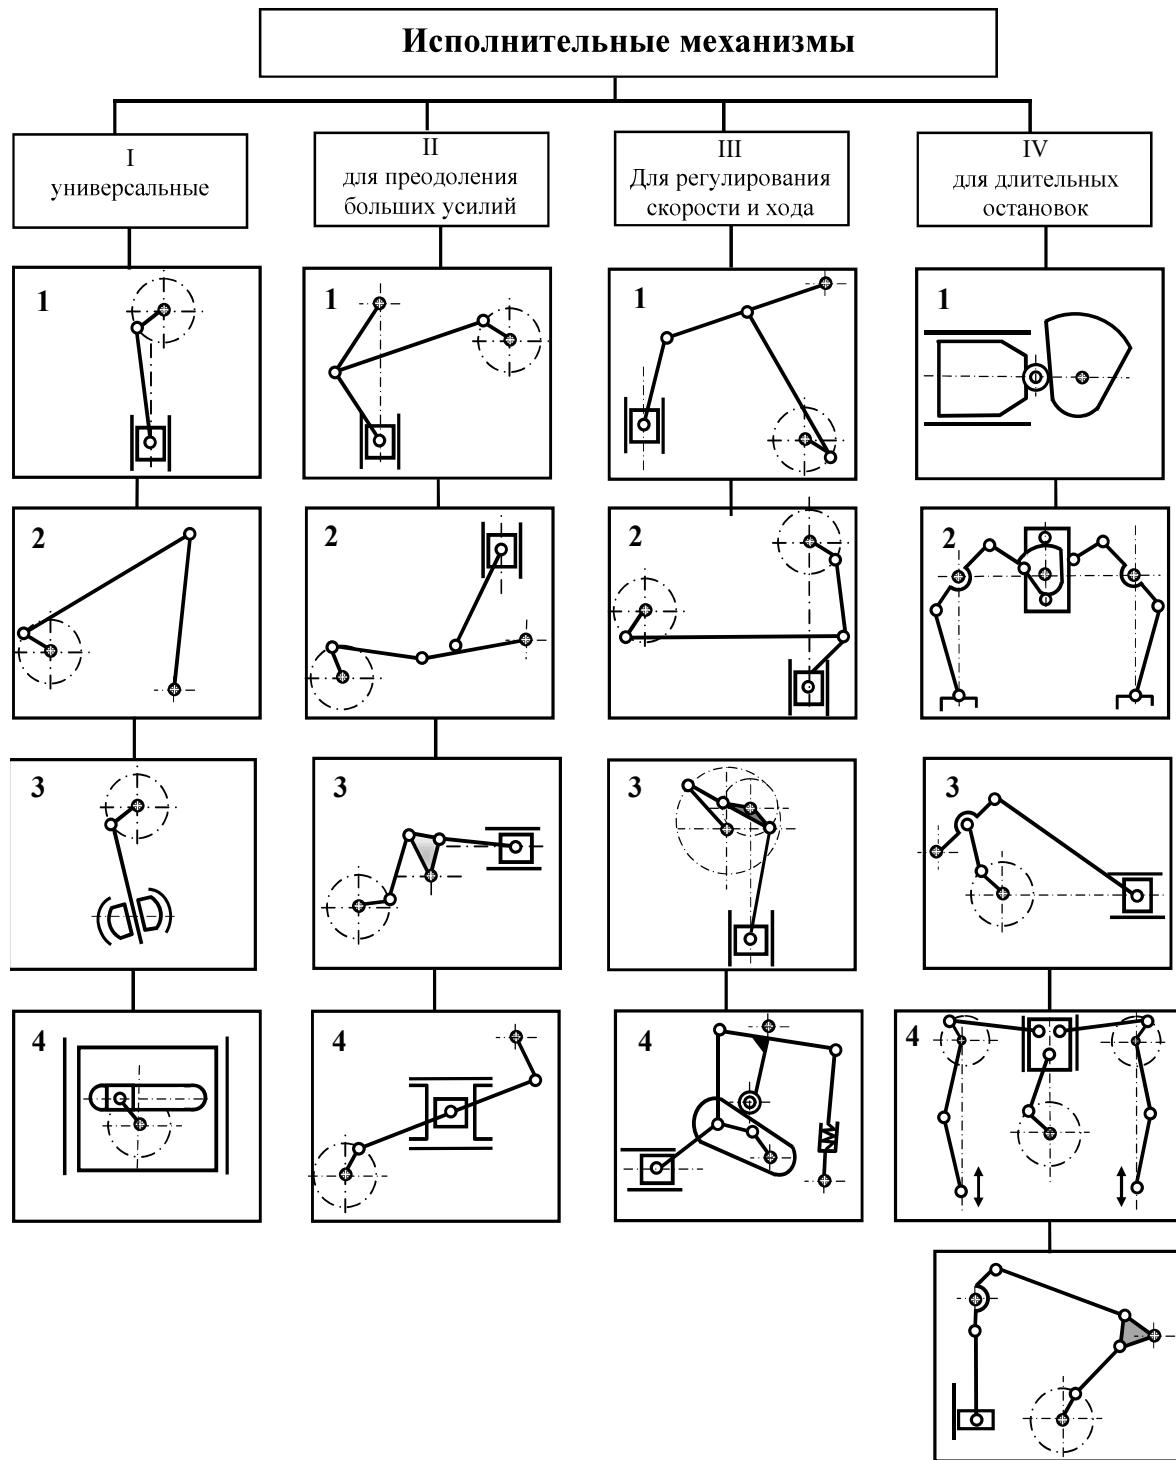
Исполнительные механизмы кривошипных прессов
